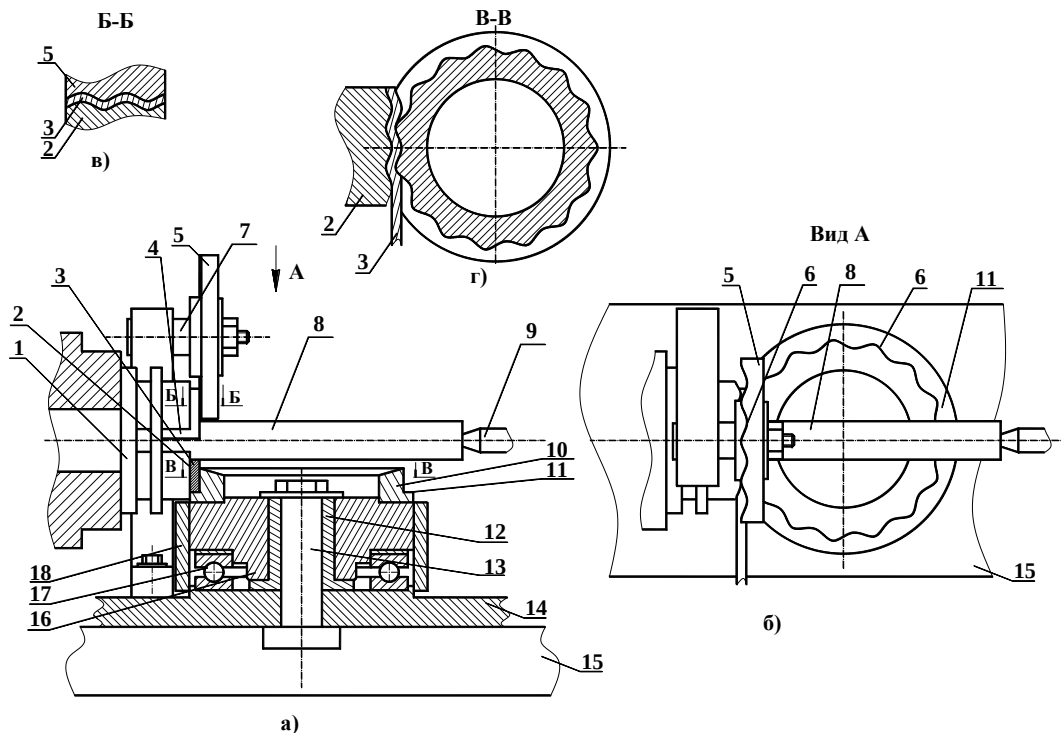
Пристрій для виготовлення гофрованих гвинтових заготовок:
